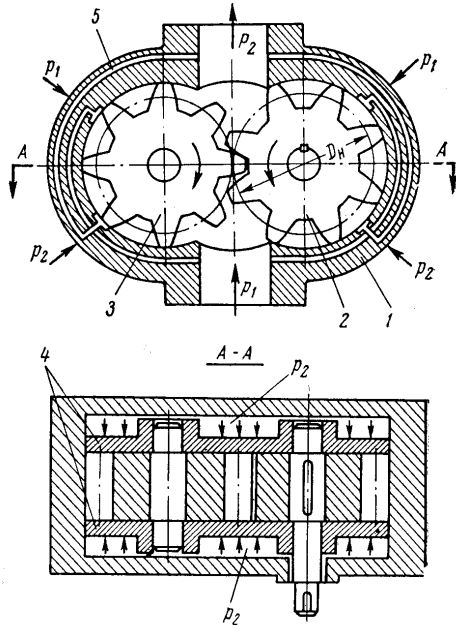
Шестеренчаста гідромашина: 1 – корпус; 2 – ведуча шестерня; 3 – ведена шестерня; 4 – торцеві диски; 5 – розвантажувальні канали
